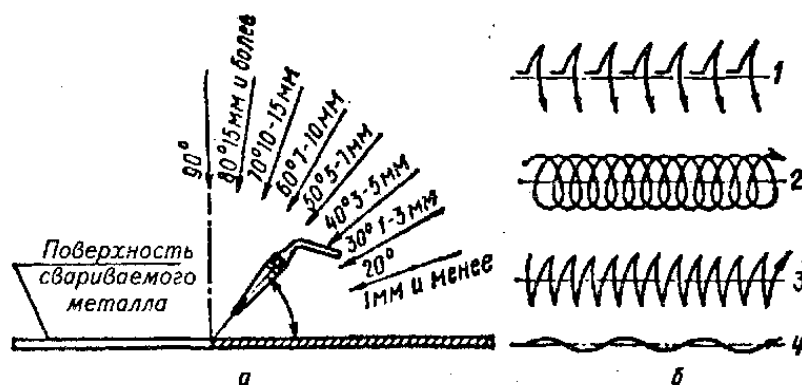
Углы наклона мундштука горелки при сварке различных толщин, — а и способы перемещения мундштука горелки — б: 1 — с отрывом горелки; 2 — спиралеобразный; 3 — полумесяцем; 4 — волнистый
